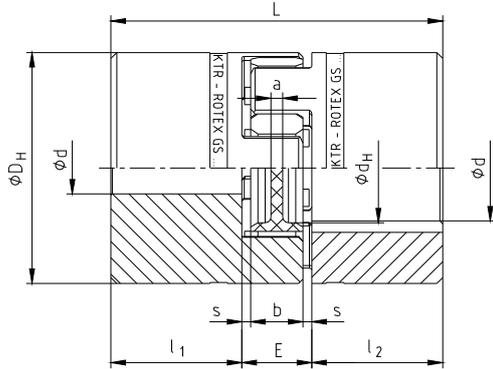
ROTEX® GS, типоразмеры 5 - 38
